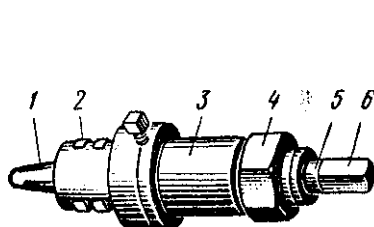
Спеціальна вальцівка: 1 — конус; 2 — ролики; 3 — корпус; 4 — гвійк; 5 — стержень; 6 — головка
